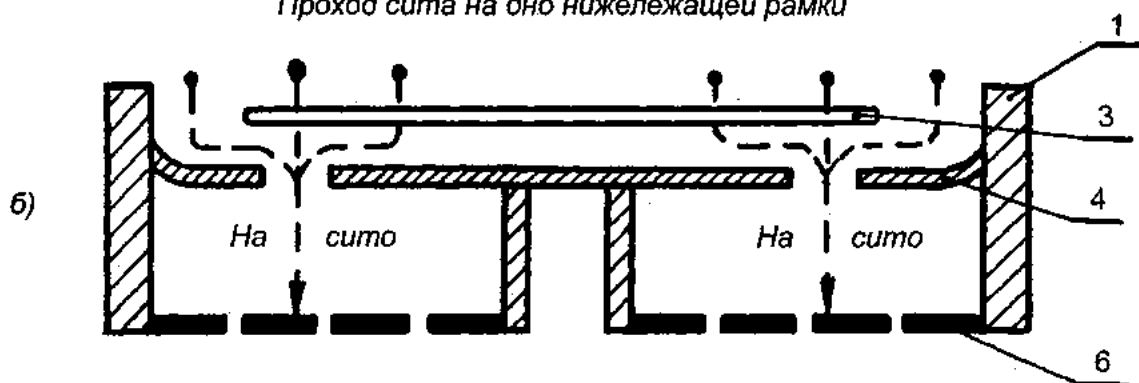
Конструктивная схема ситовой рамы пакетного отсева:
